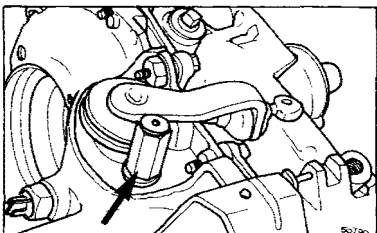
Резьбовой ограничительный стопор на 4-х ступенчатой коробке передач
